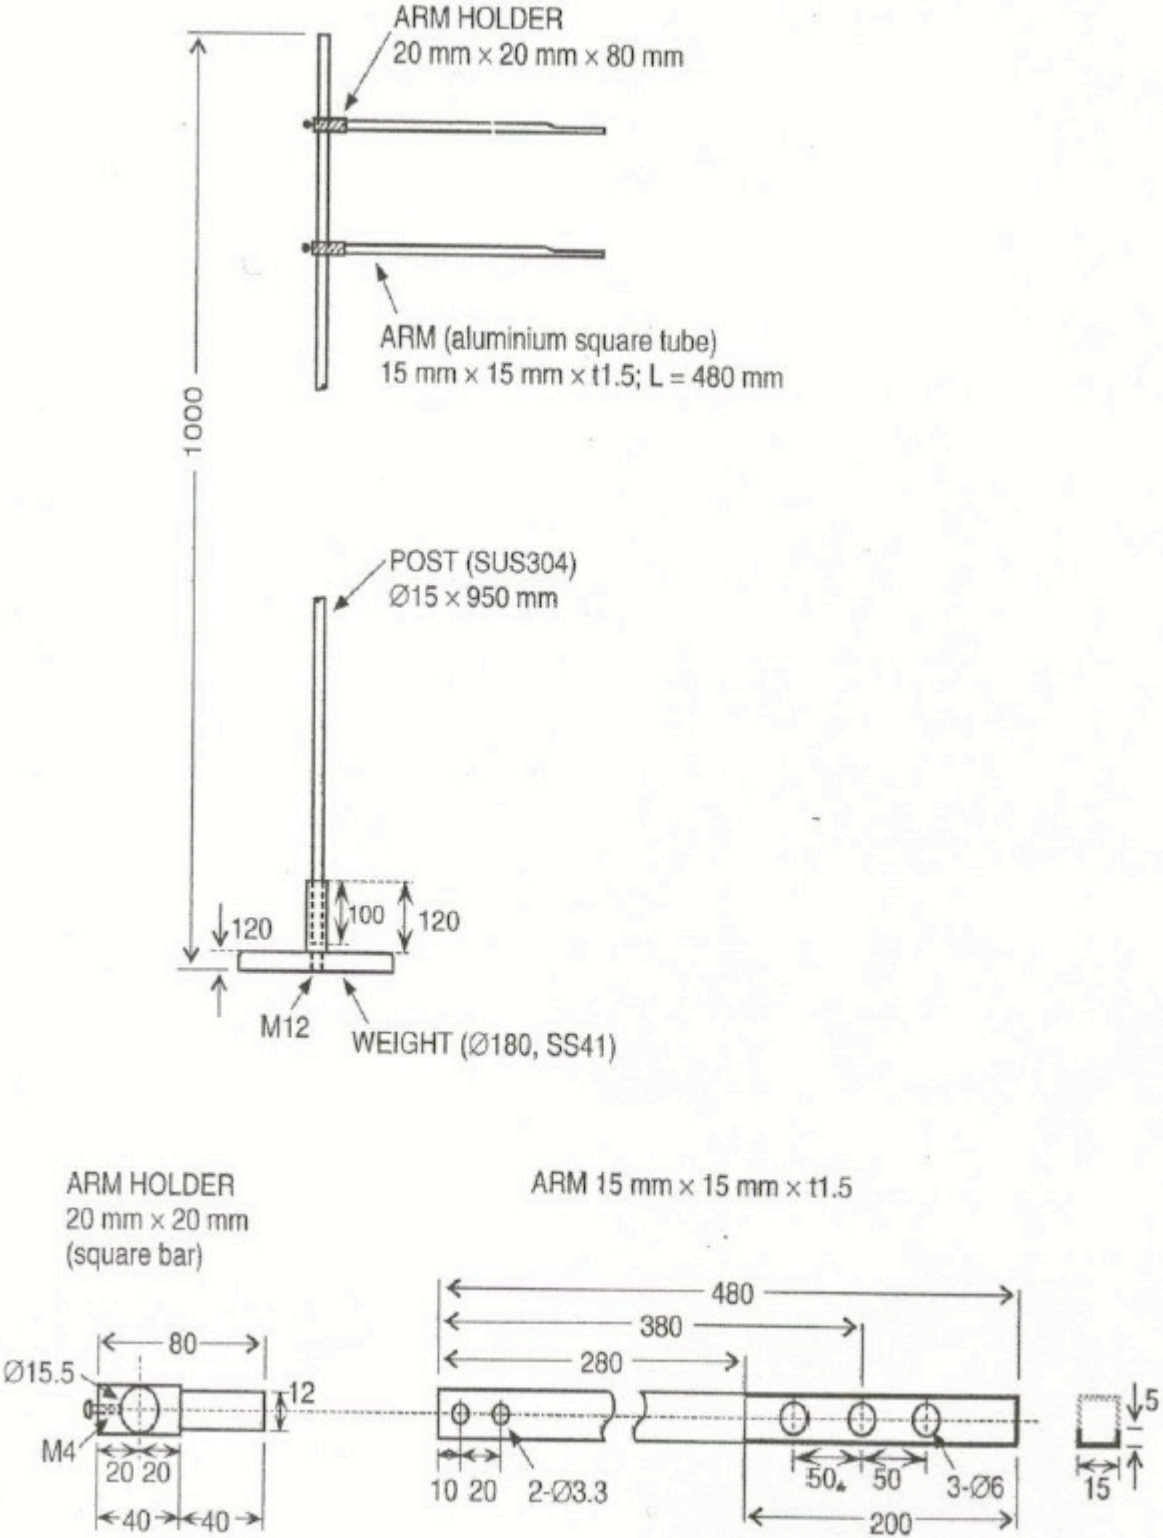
Haltevorrichtung für die Messstäbe
